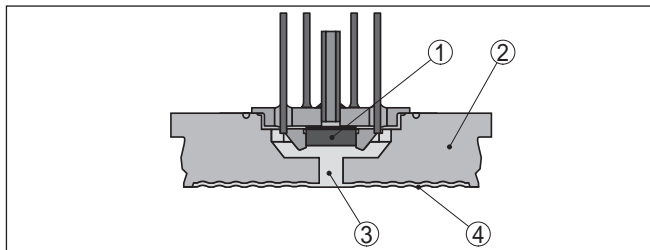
Estrutura do sistema de medição com elemento sensor piezo-resistivo
